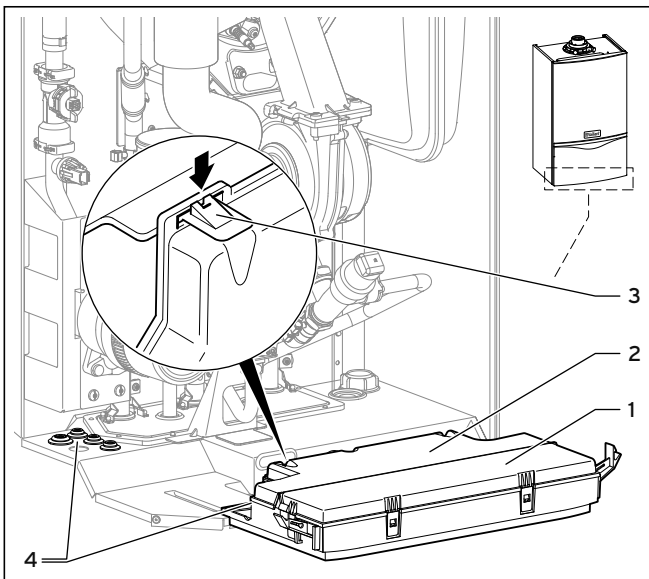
Ouverture de la paroi arrière du boîtier électronique
